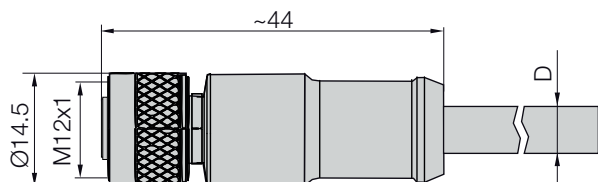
Steckverbinder mit Stecker M12, 12-polig
